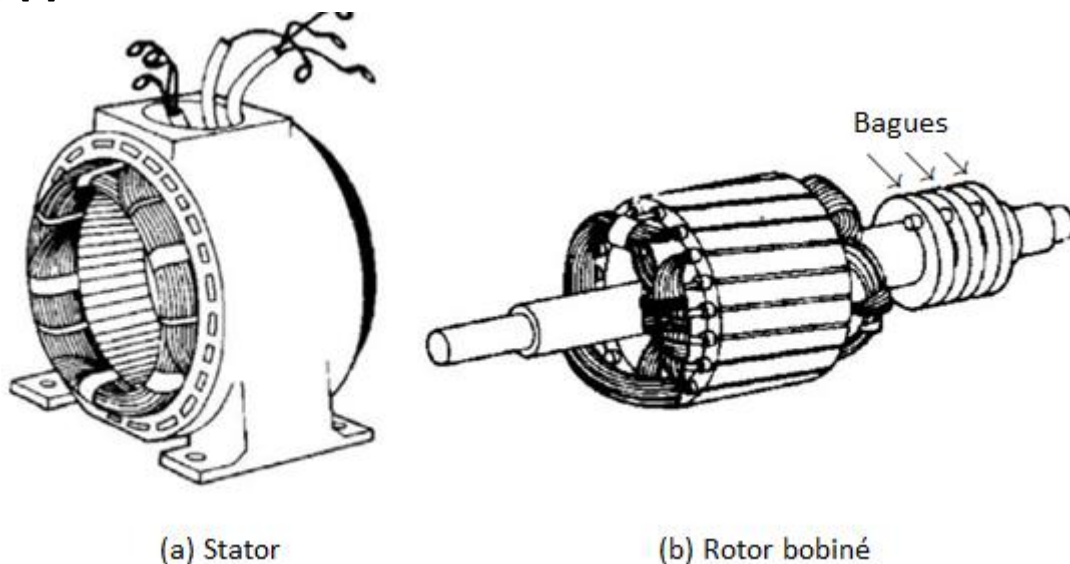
Schéma d'une machine asynchrone à rotor bobiné.
